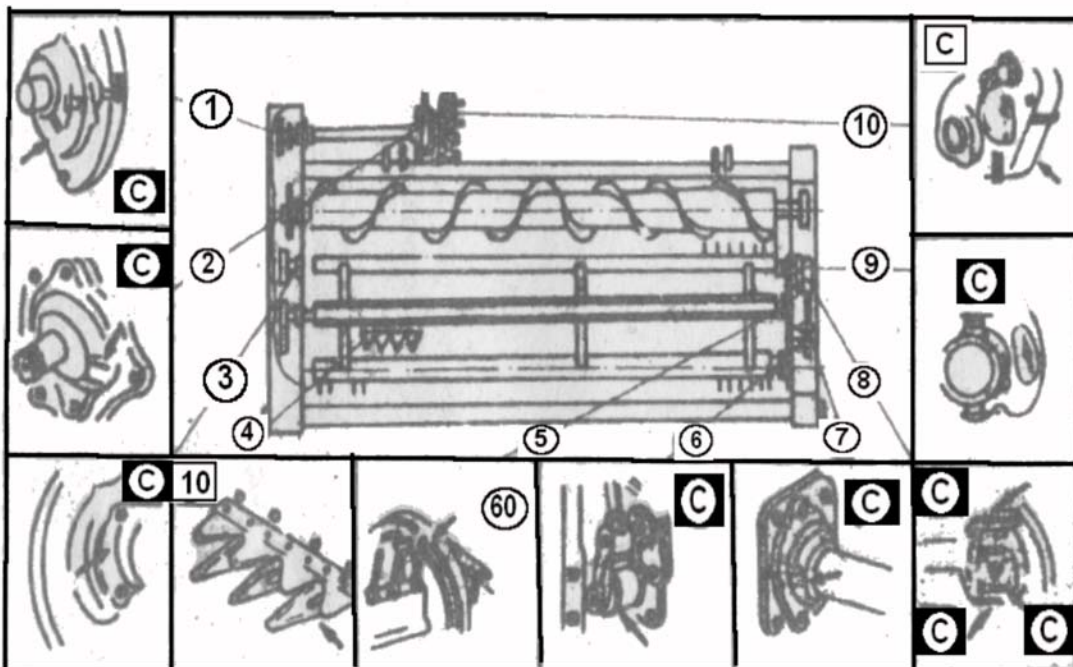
Схема смазки жатки для трав с кривошипно-шатунным механизмом качающейся шайбы открытого типа привода режущего аппарата
